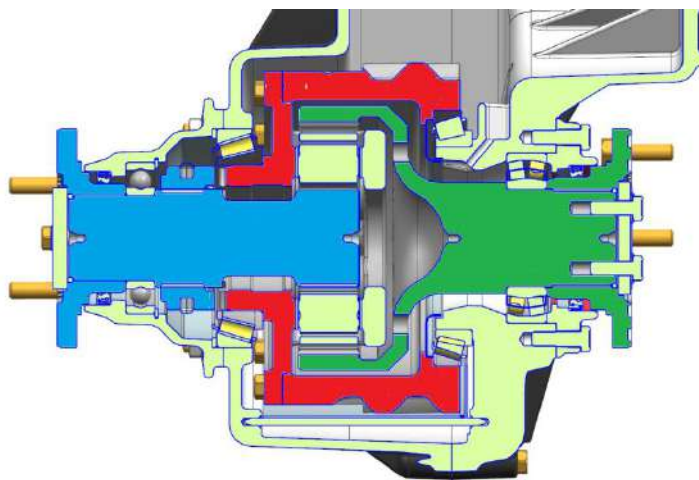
Общий вид конструкции муфты блокировки межосевого дифференциала
